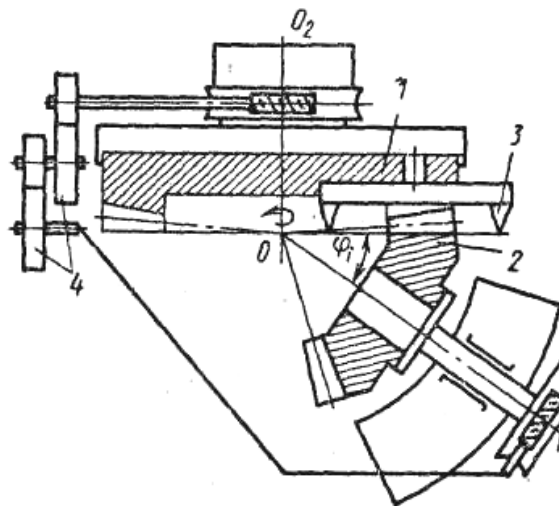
Схема установки заготовки при нарезании круговых зубьев
